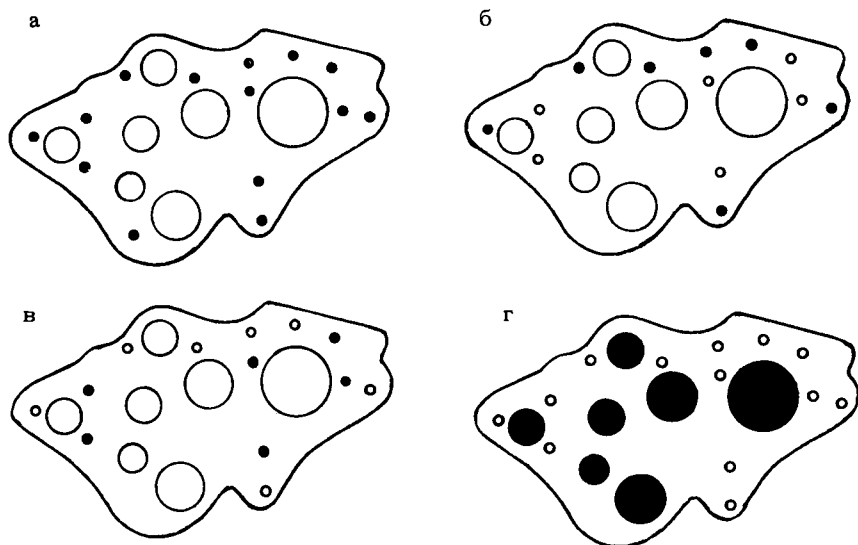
Эскиз детали, обрабатываемой на многооперационном станке.
